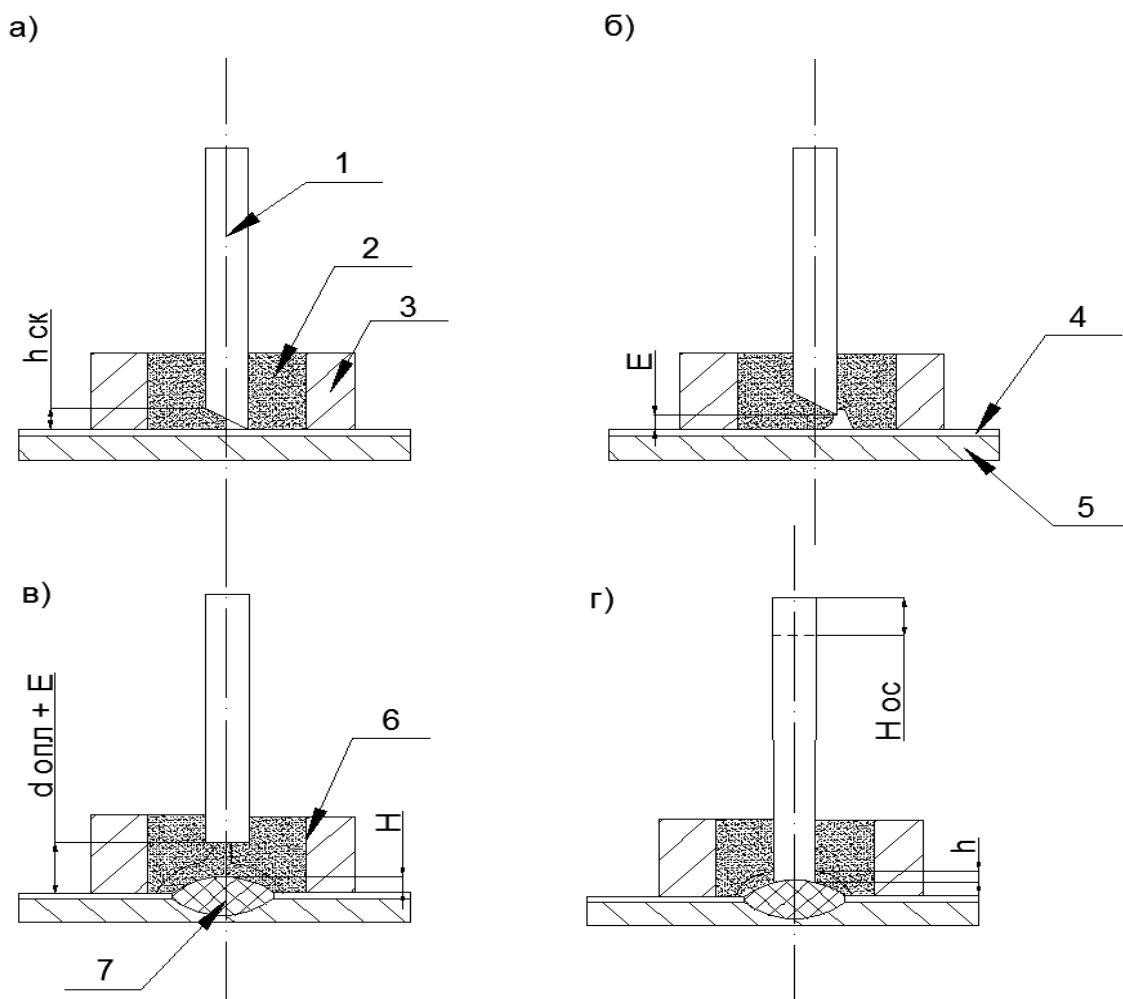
Основные этапы процесса приварки стержневых анкеров из арматурной стали
